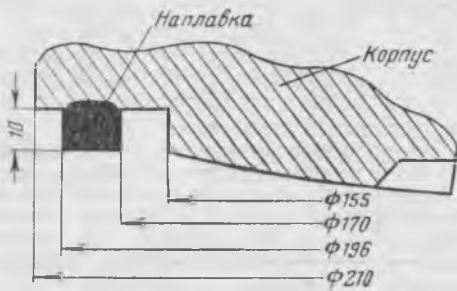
Наплавка уплотнительного кольца на корпус тарелки  $D_y = 175$  мм.
